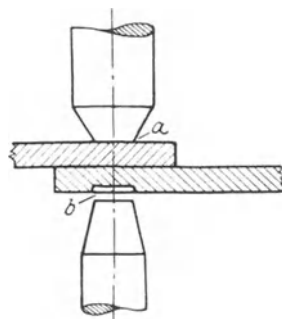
Elektroden für einseitige Schweißindrücke.
